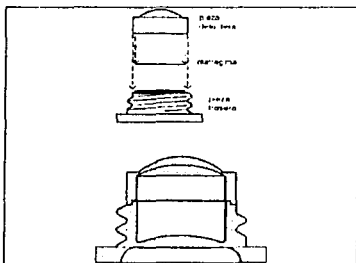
Despiece lateral y corte del objetivo-montura integral. Diseño: D.I. Gastón González Huerta/RRN.
